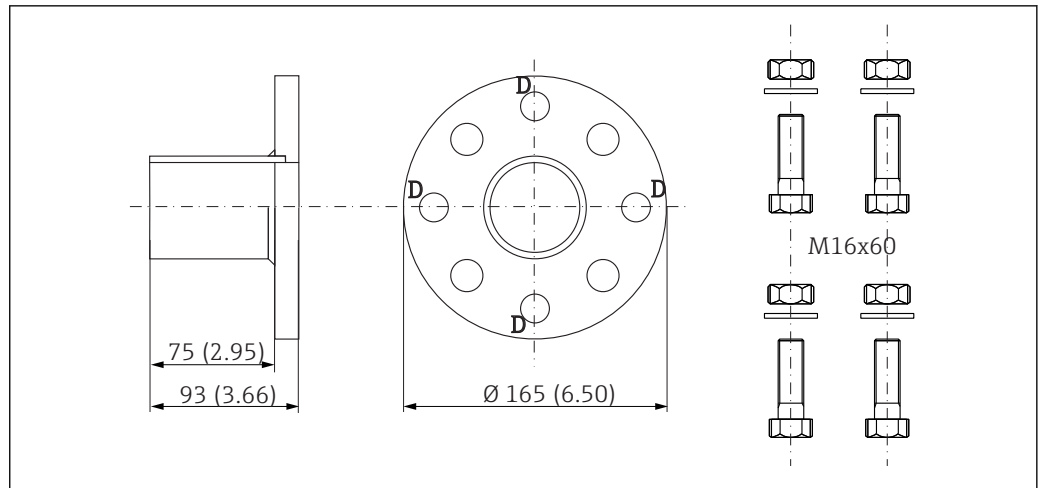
Solda do encaixe, dimensões em mm (pol.)
